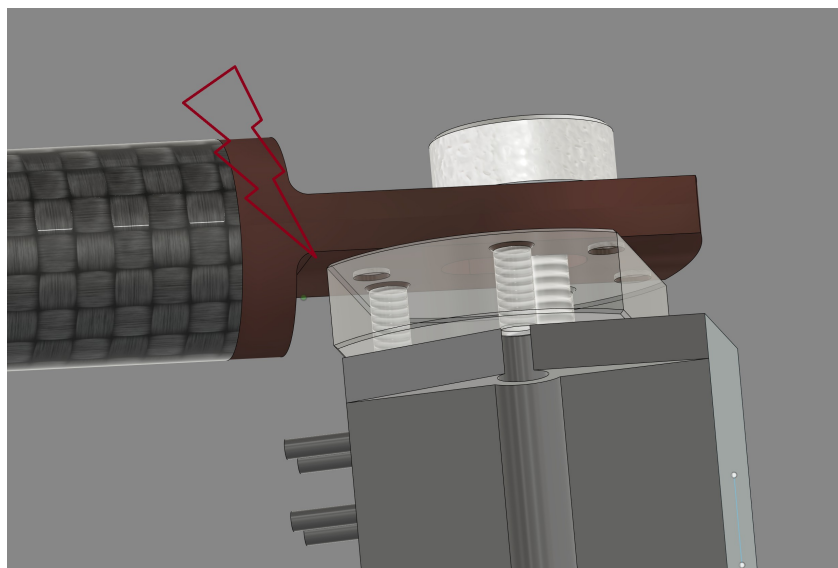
die Montageplatte muss an dieser Stelle Abstand zum Headshell haben
